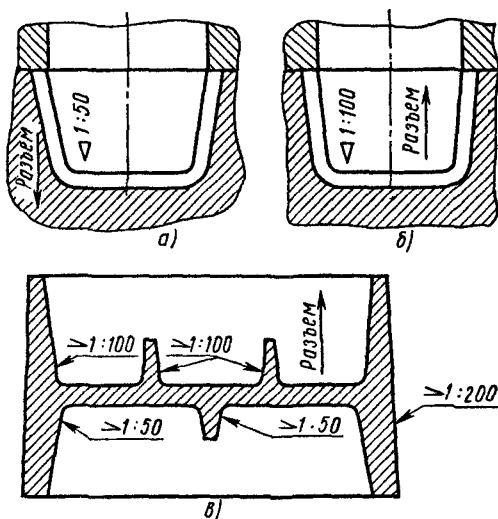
Уклоны поверхностей деталей, получаемых литьем под давлением
